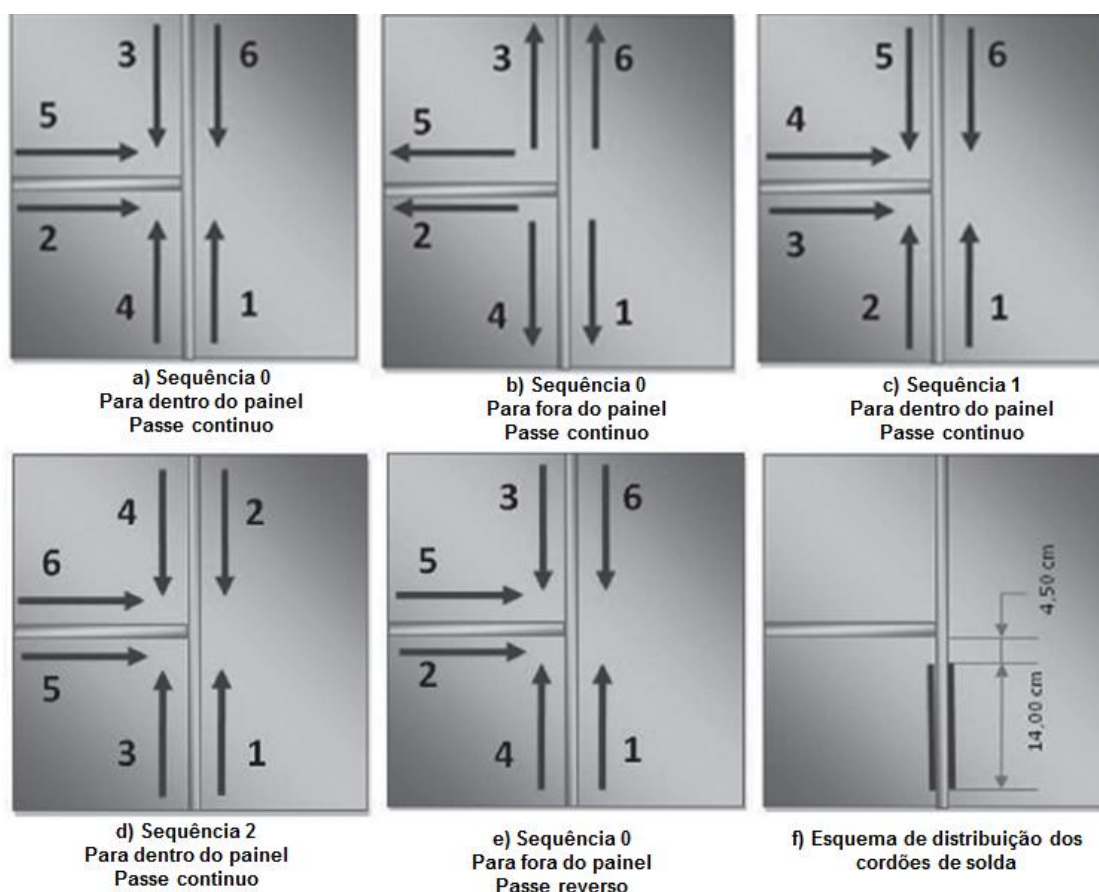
Sequências de soldagem e distribuição dos cordões de solda (CABRAL, et al., 2013).
